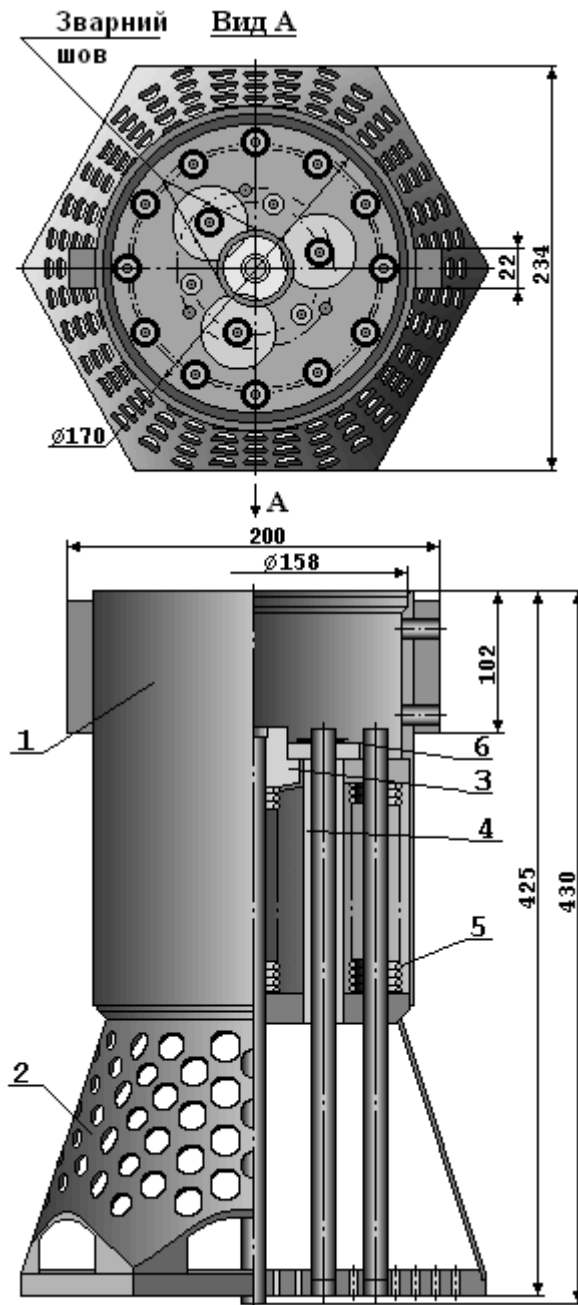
Головка базової ТВЗ реактора ВВЕР-1000:
